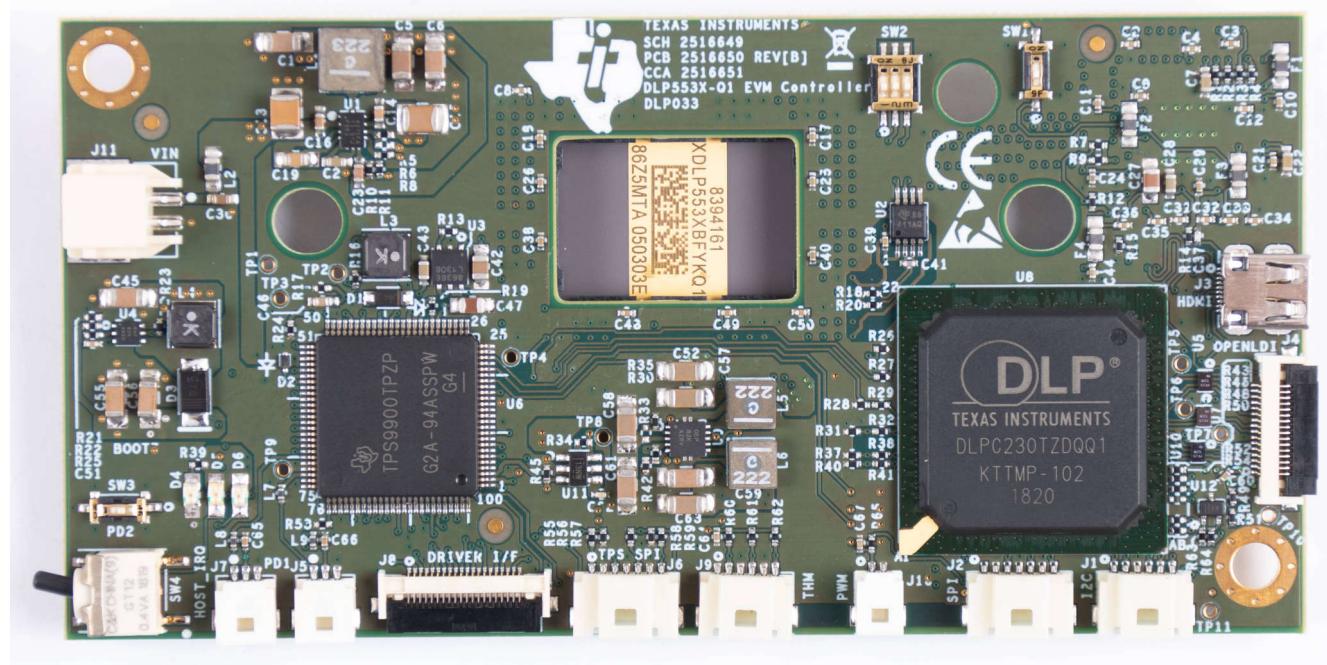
DLP5532PROJHBQ1EVM コントローラ PCB
